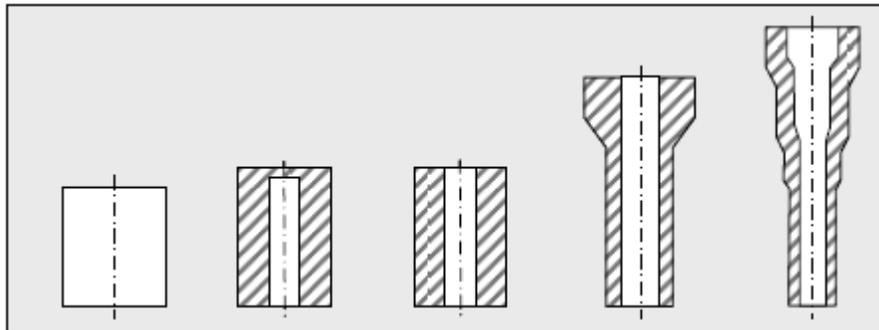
Eje de transmisión hueco; forjado hueco en vez de taladrar el agujero posteriormente. Fuente: Hirschvogel, Schrader, "Tooling Solutions for Challenges in Cold Forging".
